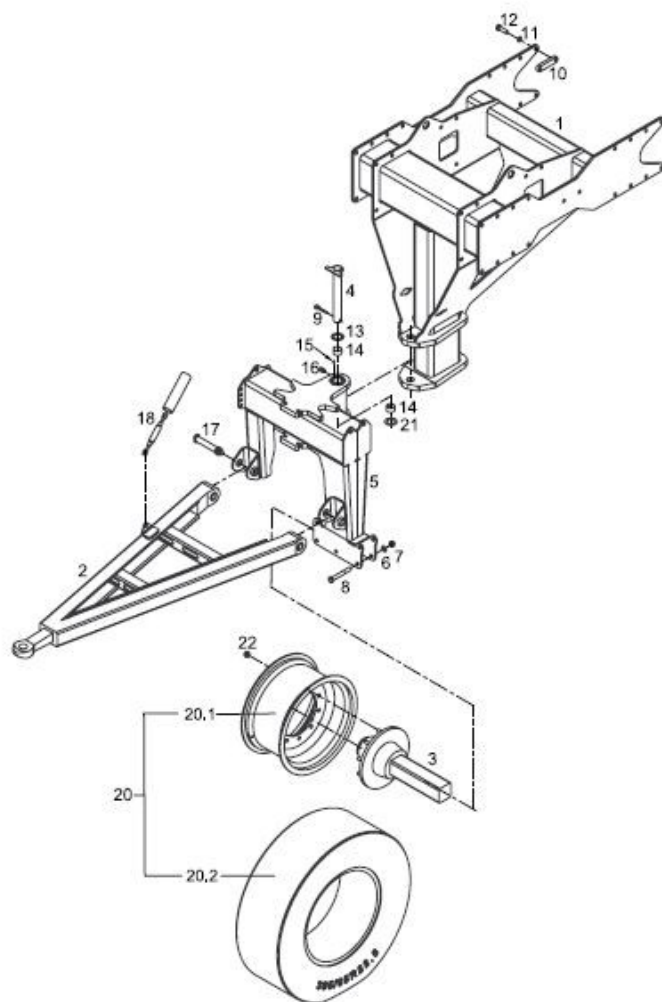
Požadované zapojení Letištního motorového zametače TJS-420.
